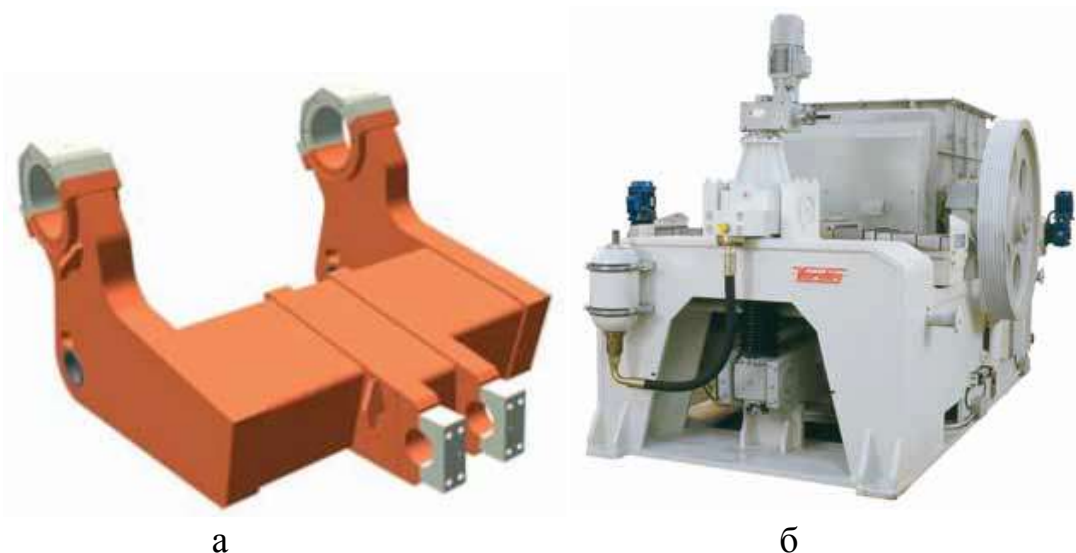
Важіль а), та загальний вид б) дробарки.
